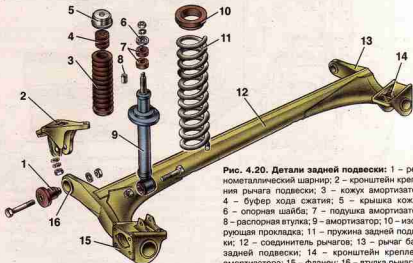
Детали задней подвески: 1 — резинометаллический шарнир; 2 — кронштейн крепления рычага подвески; 3 — кожух амортизатора; 4 — буфер хода сжатия; 5 — крышка кожуха; 6 — опорная шайба; 7 — подушка амортизатора; 8 — распорная втулка; 9 — амортизатор; 10 — изолирующая прокладка; 11 — пружина задней подвески; 12 — соединитель рычагов; 13 — рычаг балки задней подвески; 14 — кронштейн крепления амортизатора; 15 — фланец; 16 — втулка рычага
